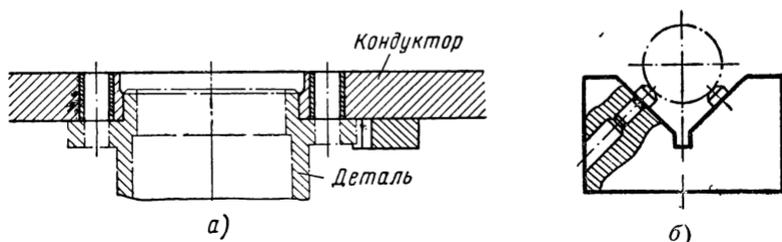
Схема установки детали по внешней цилиндрической поверхности:
